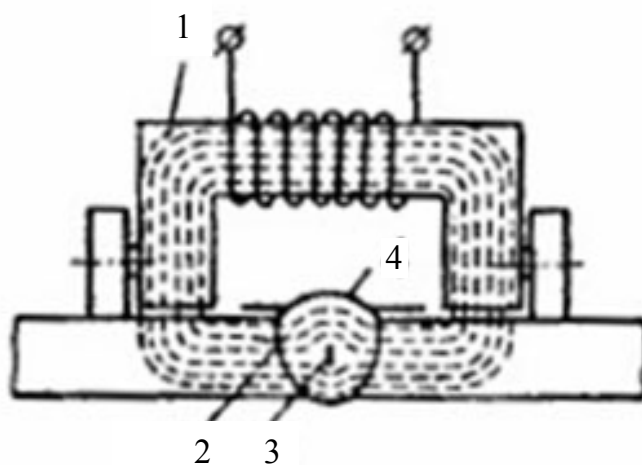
Проверка качества сварных швов магнитной дефектоскопией:
